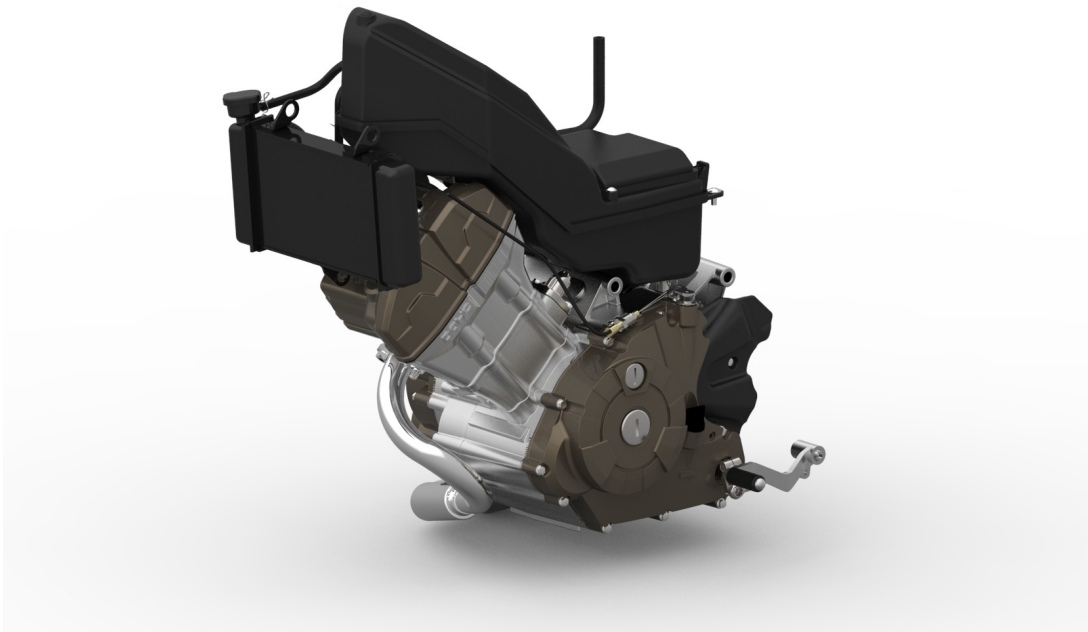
CAD-Rendering des Prototypenmotors
